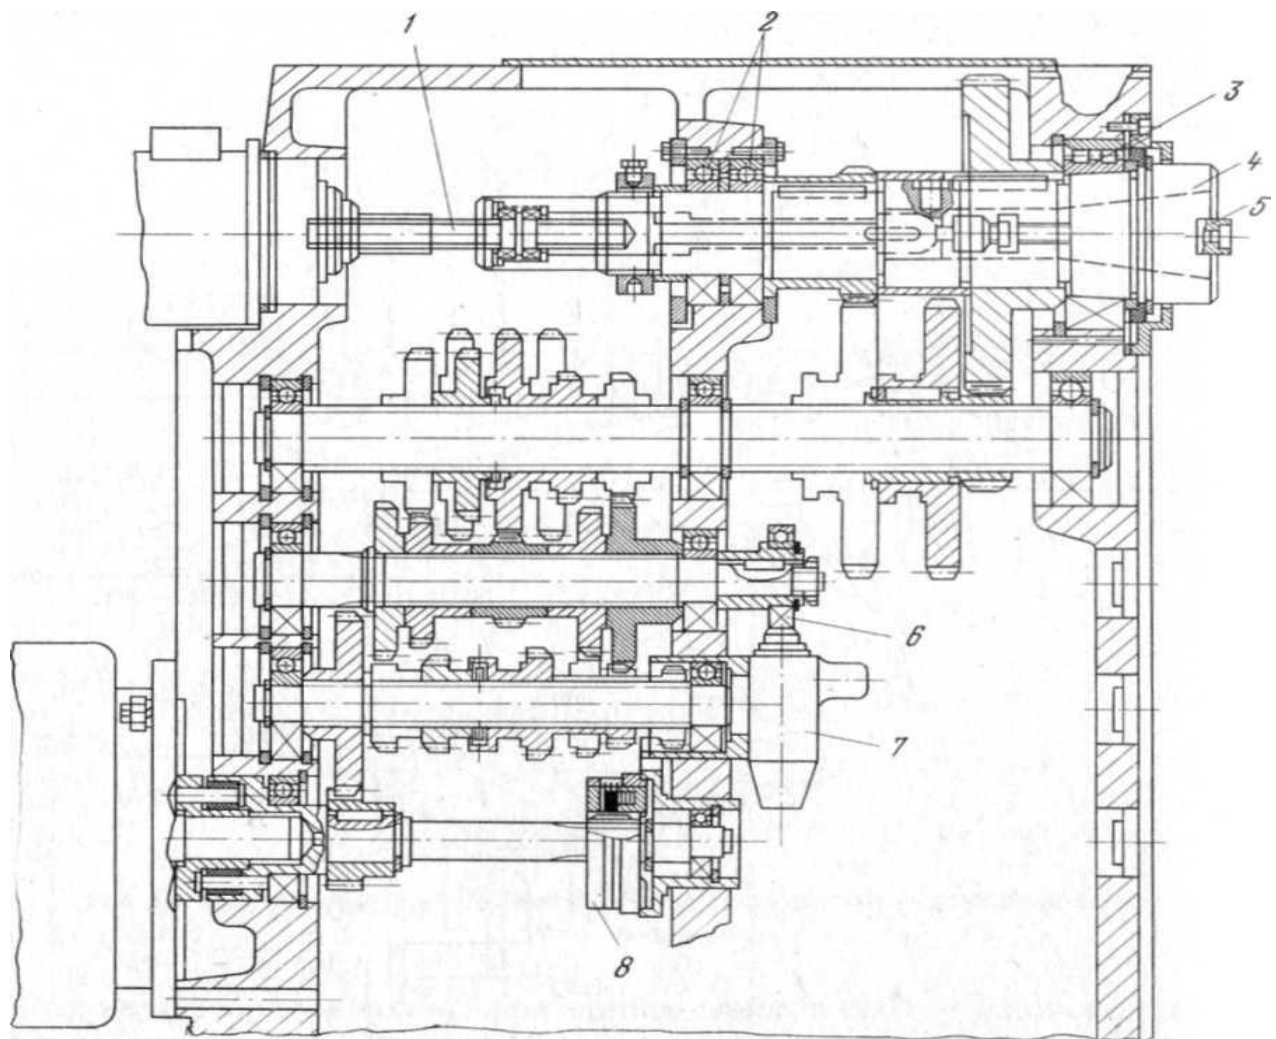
Привод главного движения горизонтально-фрезерного станка.
